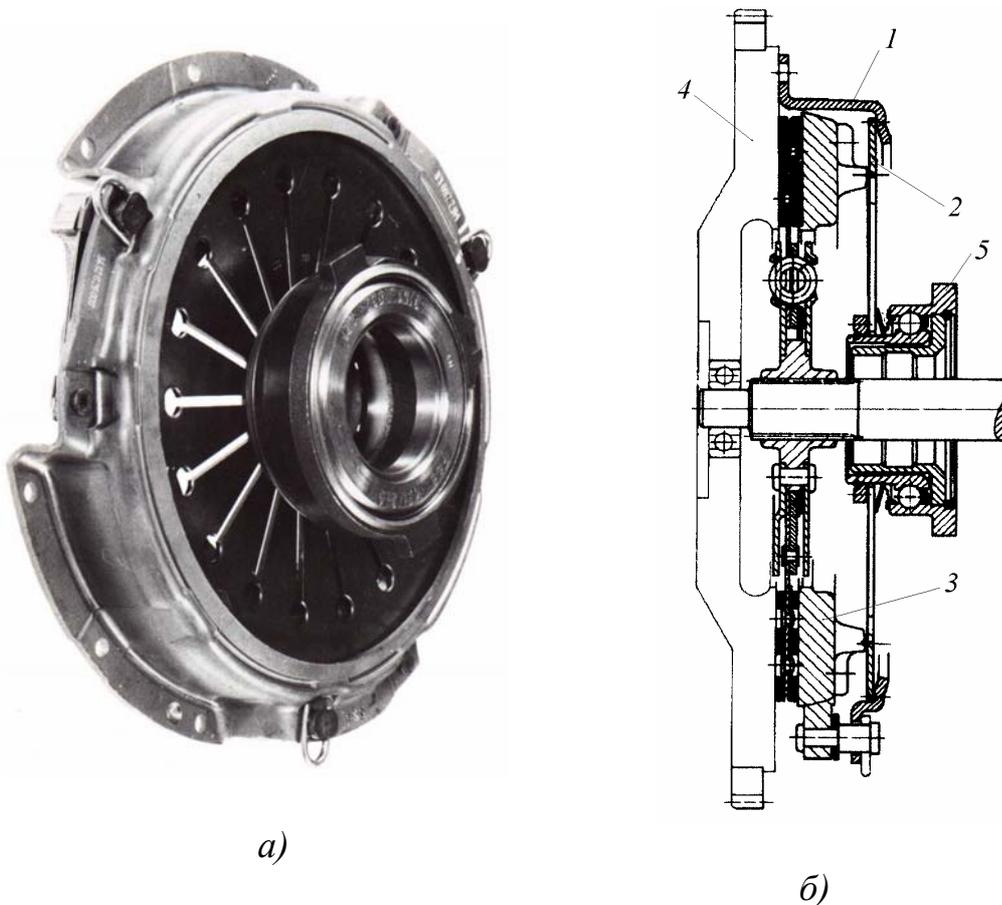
ФС с обратной установкой разрезной тарельчатой пружины:
